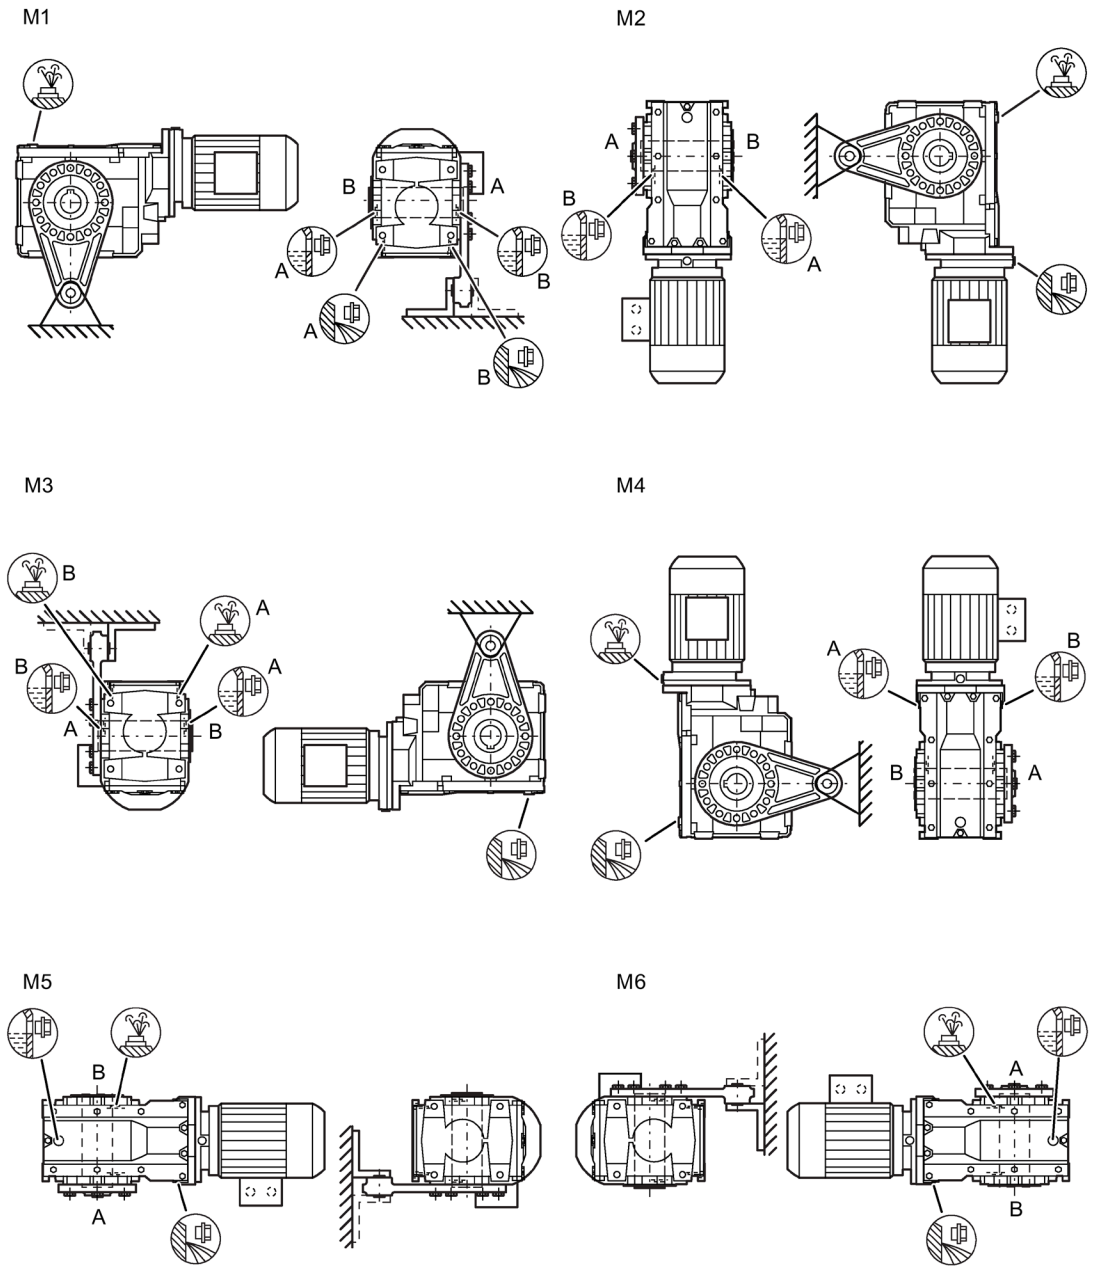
Einbaulagen für Kegelnradgetriebe BAD Aufsteckausführung Baugrößen 39 - 49
